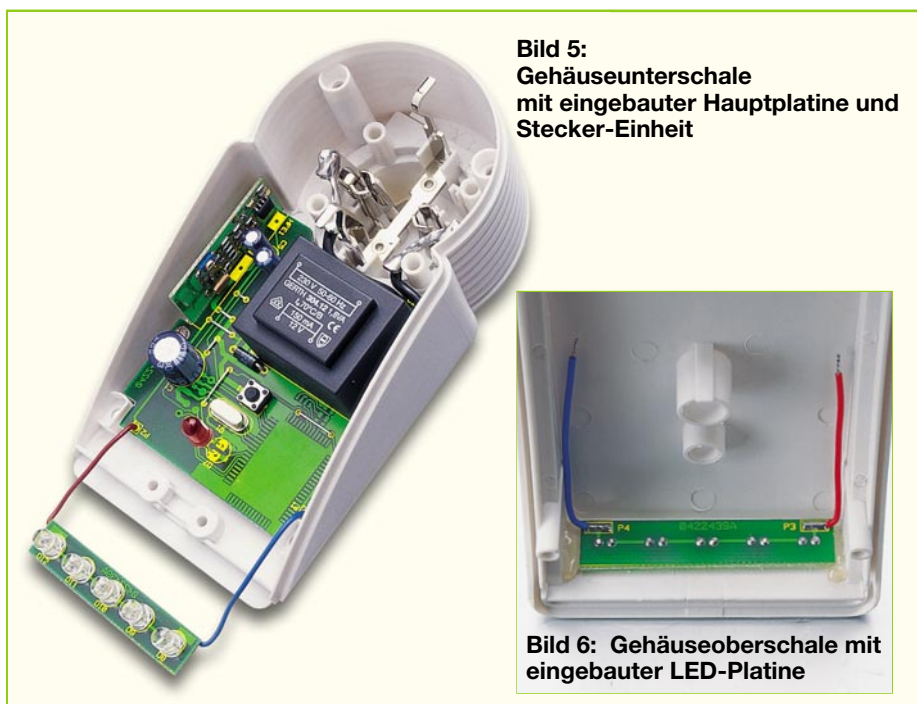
Gehäuseunterschale mit eingebauter Hauptplatine und Stecker-Einheit
